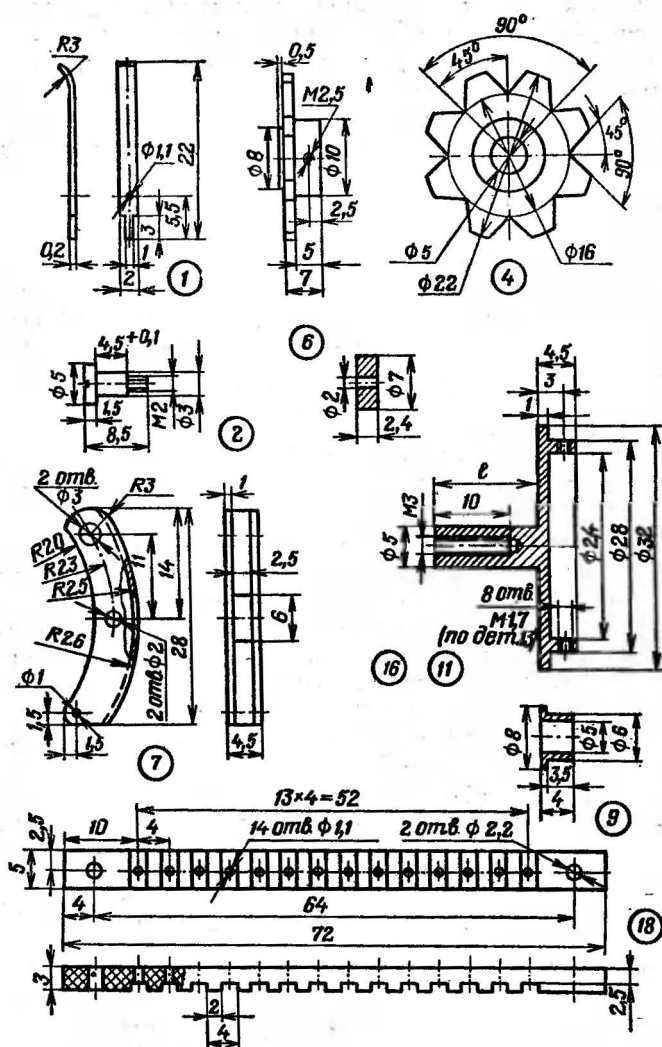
Детали переключателя: 1 — контакт неподвижный, Бр.Б2, серебрить; 2 — винт специальный, Ст.20; 4 — звездочка, Д16-Т; 6 — ролик, Ст.20; 7 — коромысло, ЛС59-1; 9 — втулка, Ст.20; 11, 16 — полуоси малая и большая. Размер  $l$  дет. 11 равен 14 мм, у дет. 16 — 10 мм. Деталь 16 отверстия М3 не имеет; 18 — планка
